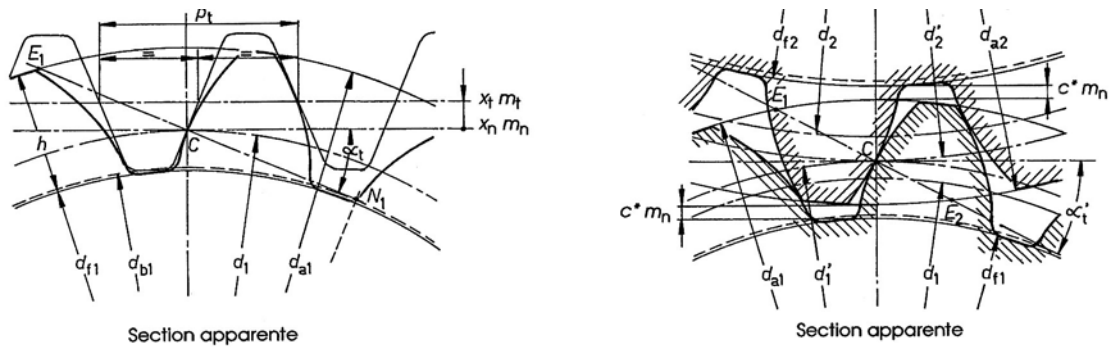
Dimensions géométriques d'un engrenage cylindrique extérieur à denture déportée
